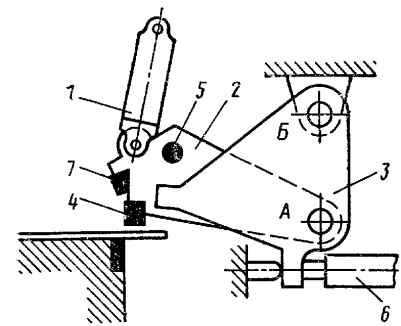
Схема ножниц для резки со скосом кромки под сварку
